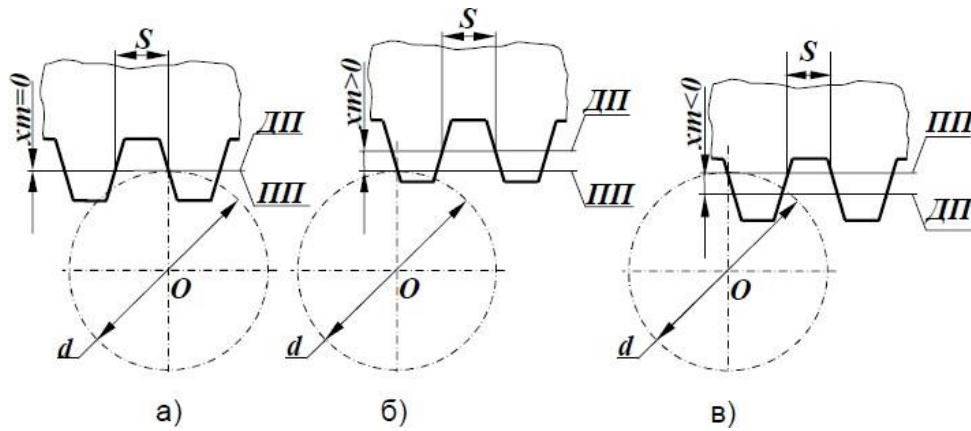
Схеми нарізування зубчастих коліс: а – нульового; б – позитивного; в – від’ємного.
